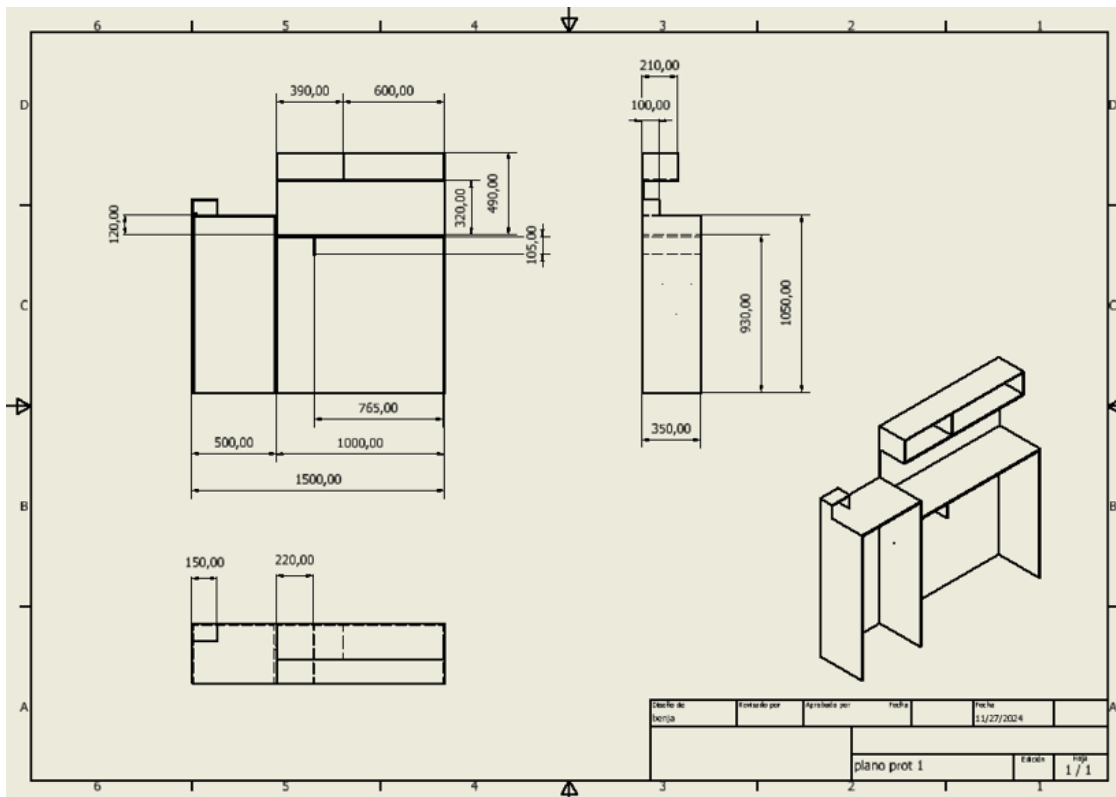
Plano con medidas de propuesta preliminar para picking.
